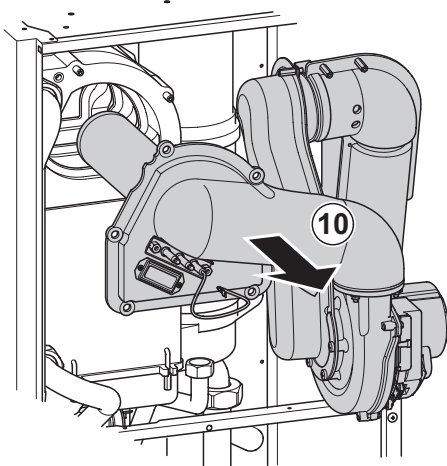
Ослабить резьбовое соединение и снять газовый распылитель.
